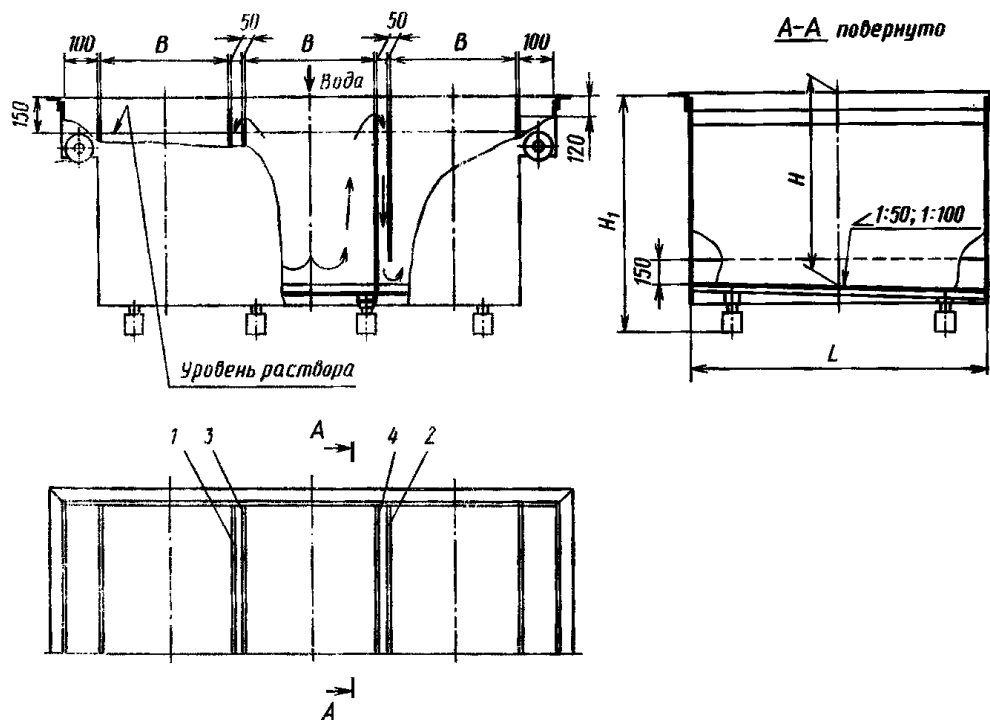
Корпус ванны двухступенчатой противоточной промывки с разделительными стенками (стенками показано направление движения чистой воды)
